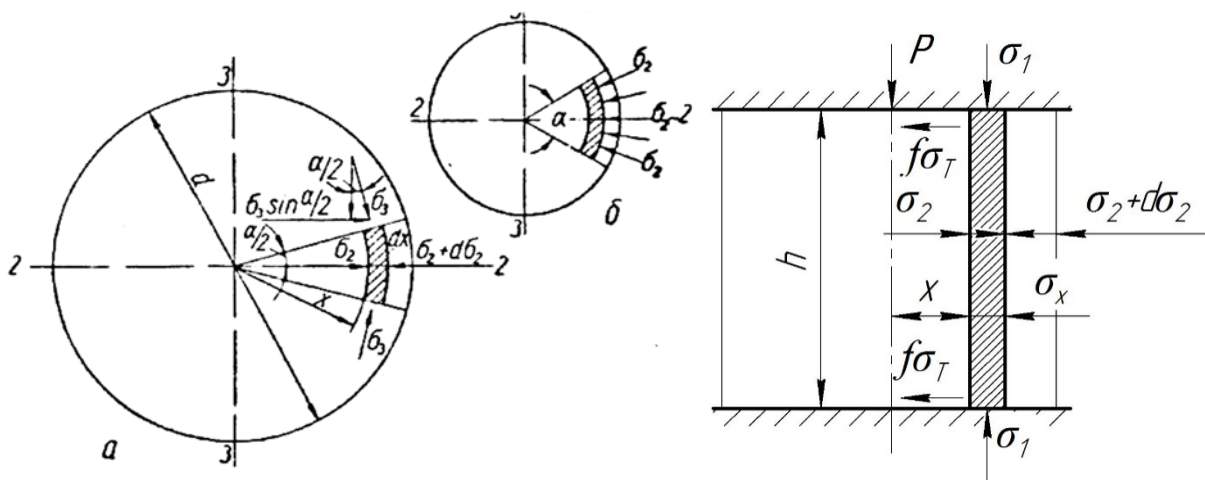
Схема сил, діючих при осаджуванні циліндричної заготовки
